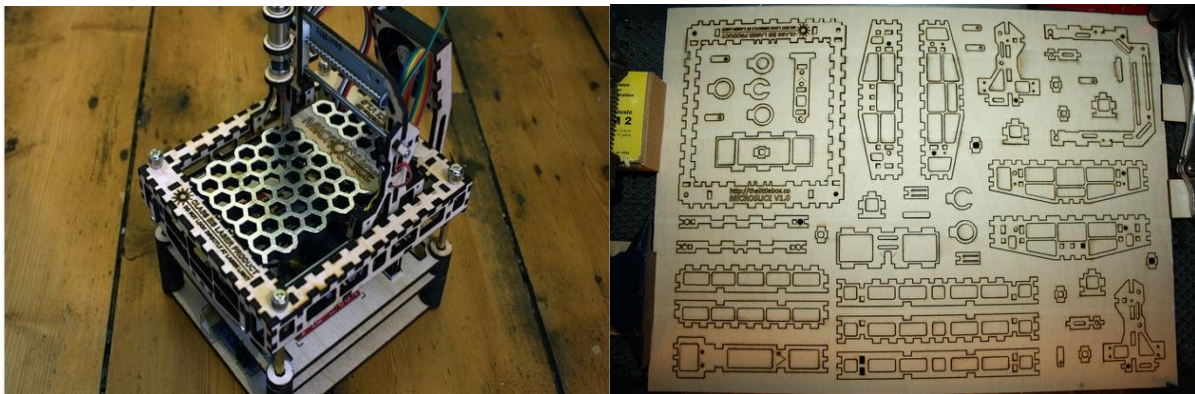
Fuente: Kickstarter . Máquina terminada y despiece previo a la fabricación
